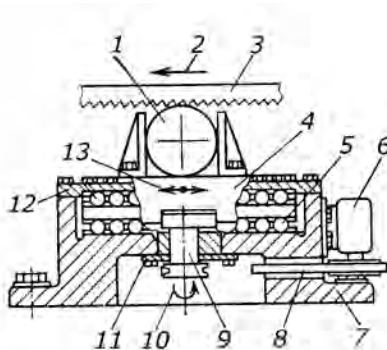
Схема станка с ленточной пилой при сообщении колебаний обрабатываемой заготовке: 1 – заготовка; 2 – направление главного движения; 3 – ленточная пила; 4 – крепежное приспособление; 5 – шариковые направляющие; 6 – электродвигатель; 7 – станок; 8 – ременная передача; 9 – эксцентриковый кулачок; 10 – вращательное движение; 11 – подшипники; 12 – крышка; 13 – колебательное движение
